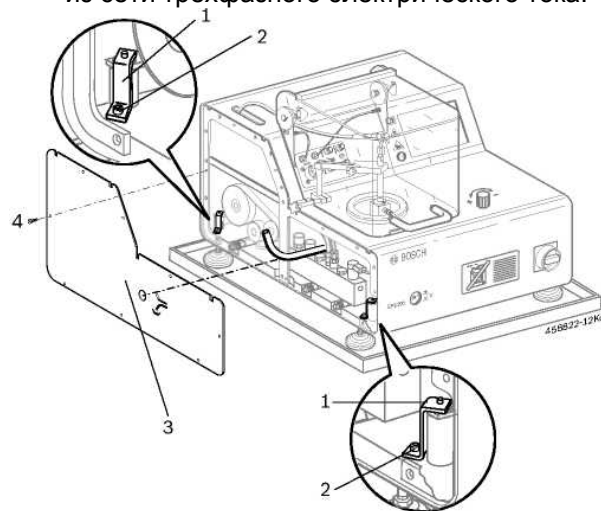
Удаление транспортировочного предохранительного приспособления.
